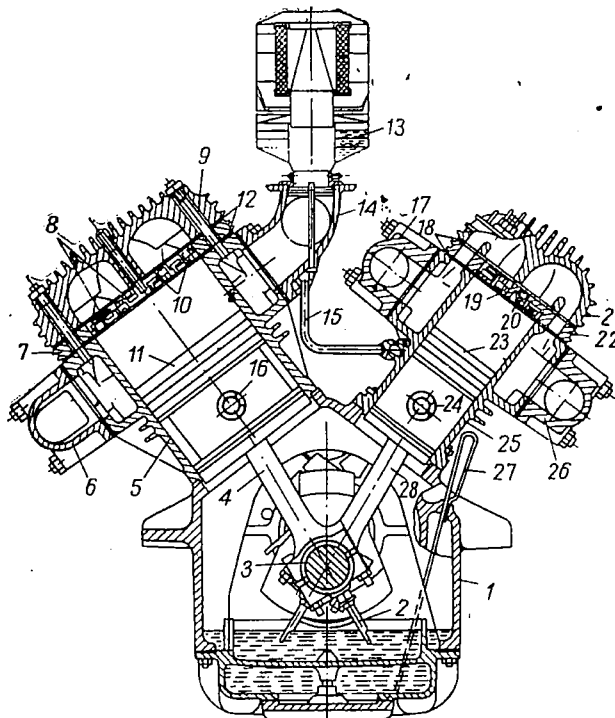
Воздушный компрессор с V-образным расположением цилиндров
